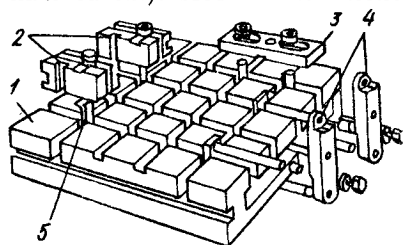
Монтажна схема УСО для фрезерних робіт:
